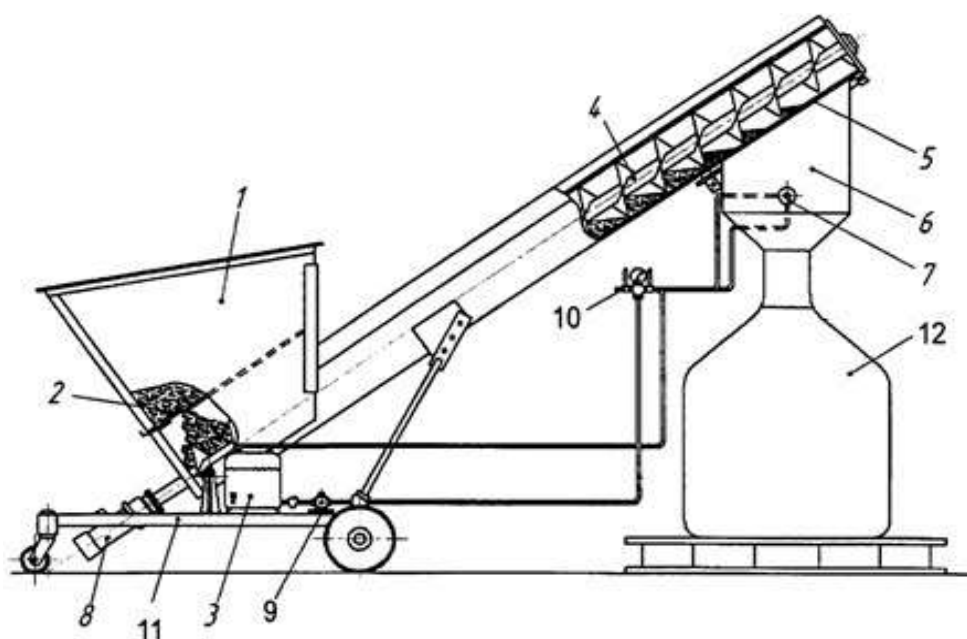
Установка шнекового типу обробки насіння: 1 – завантажувальний бункер; 2 – дозатор насіння; 3 – бак; 4 – шнек; 5 – решето; 6 – камера розпилювання; 7 – форсунка; 8 – електропривод; 9 – насос; 10 – регулятор тиску; 11 – рама; 12 – вивантажувальний бункер
